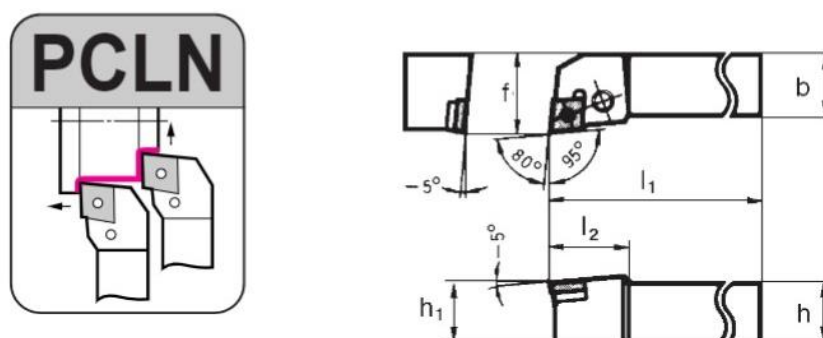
Державка PCLN R 2525 M19 [1, с. 122]
